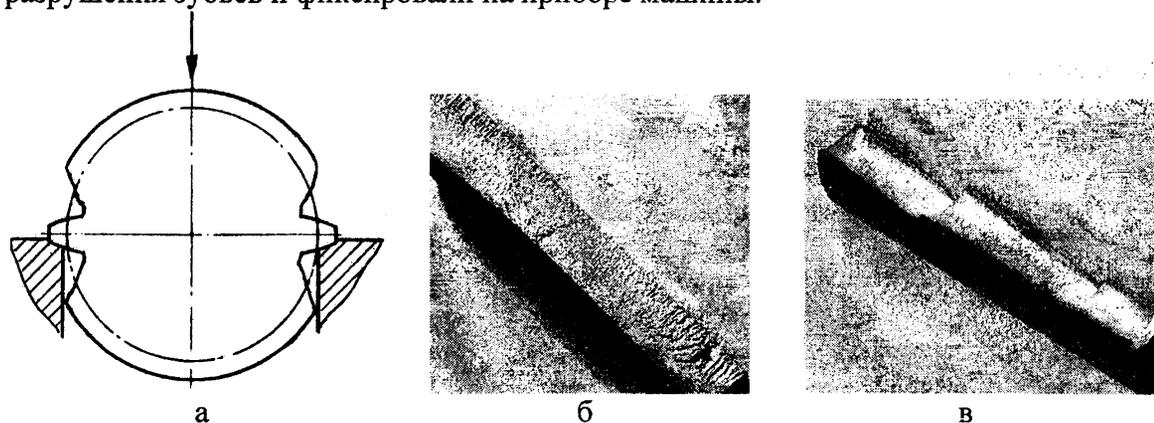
Схема нагружения шестерен колесной передачи при испытаниях на статическую прочность – а, и вид изломанных зубьев из сталей б - 60ПП, в - 20ХН3А
